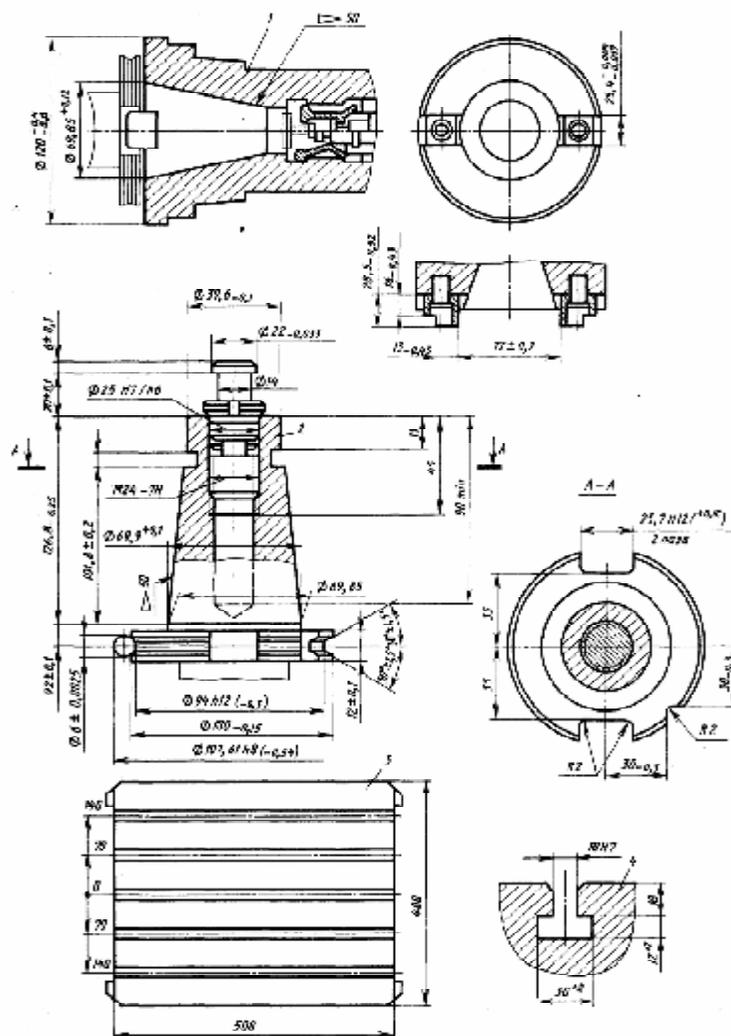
Установочные базы сверлильно-фрезерно-расточного станка мод 2254ВМФ (1- шпindelь; 2 – инструментальная оправка; 3 – спутник; 4 – паз стола и спутника)
